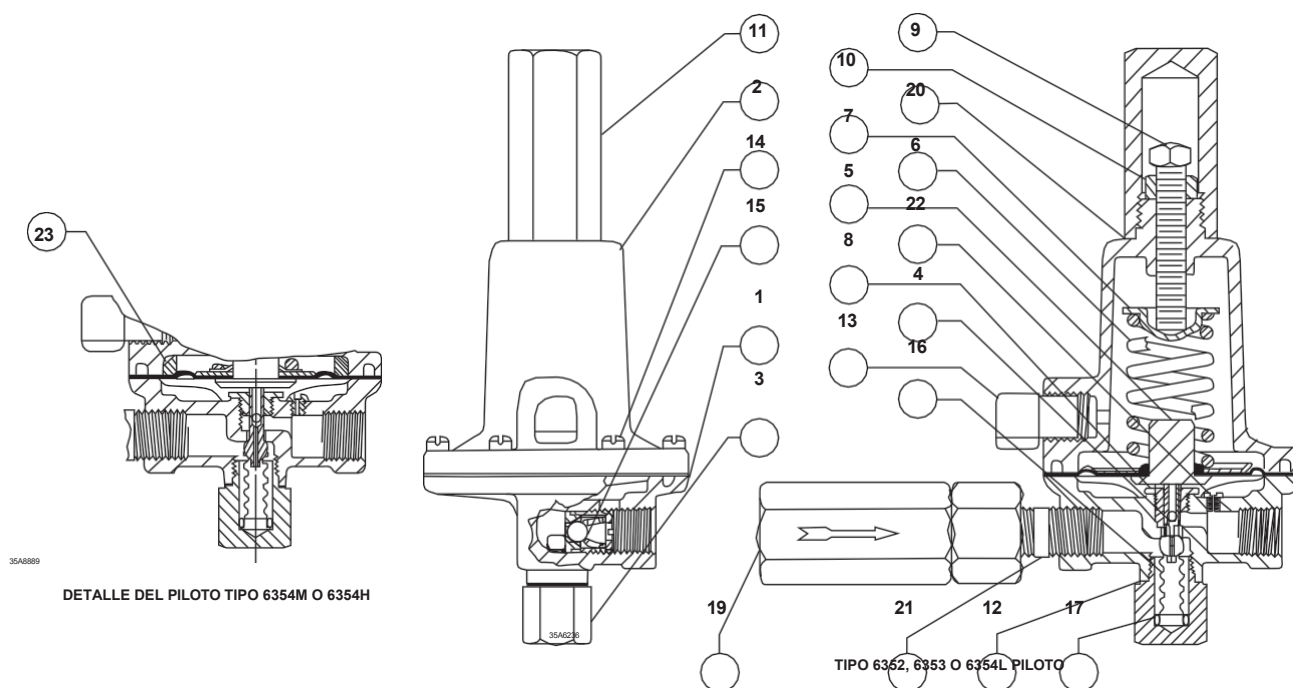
Conjuntos piloto de los tipos 6352 a 6354H
